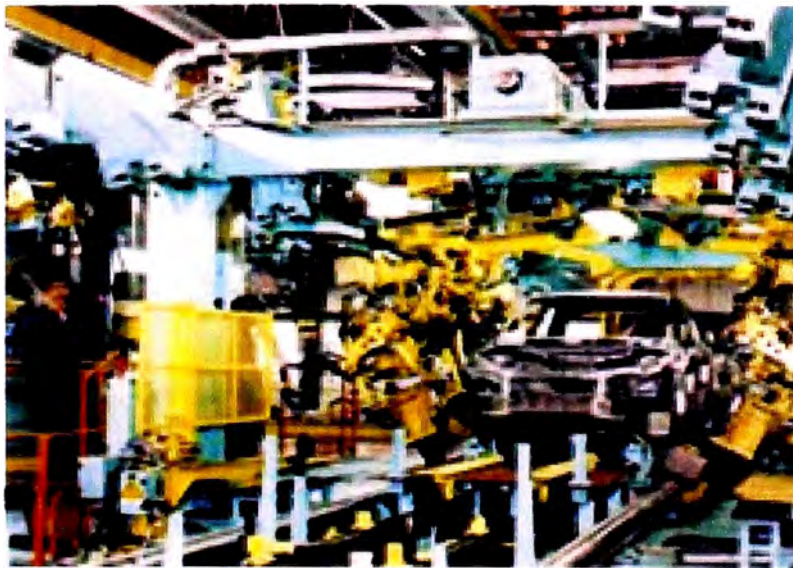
Carrocería en dispositivo de soldadura - ensamble final
